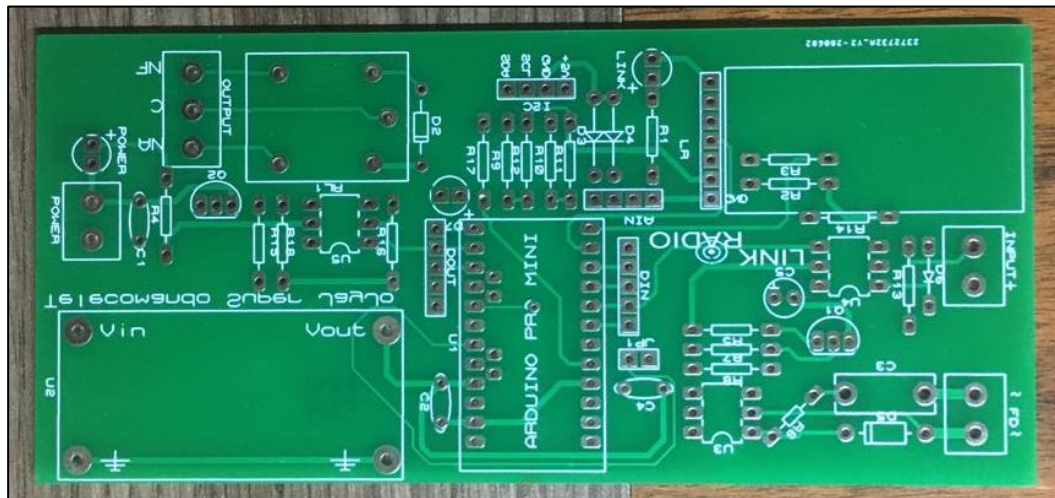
Placa de circuito impresso concluída. Fonte: Do autor.
